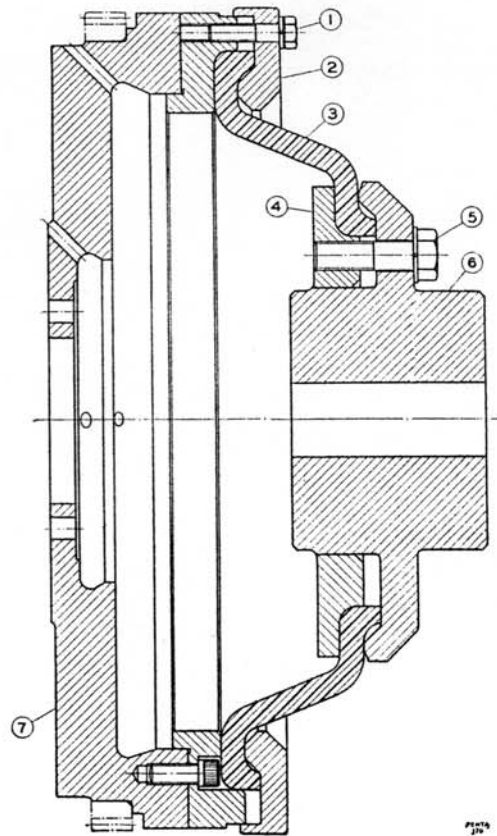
Elastische Kupplung für das Schwungrad des Motors im Schnitt.
